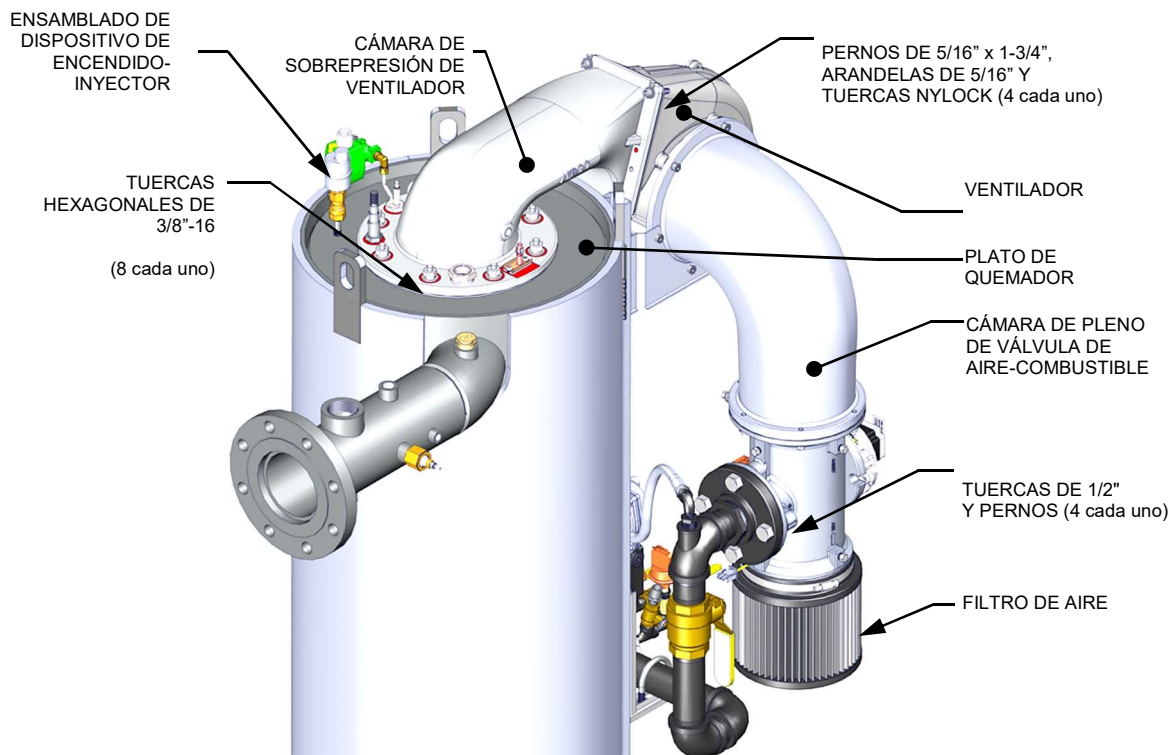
Información de montaje de ensamblado del quemador de BMK 1500/2000
